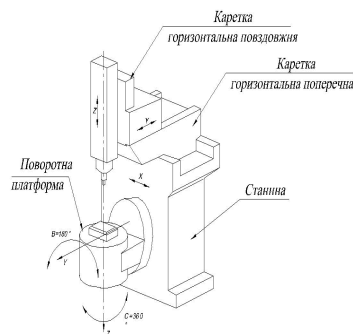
Вертикально-фрезерний консольний верстат із поворотною платформою (столом)
